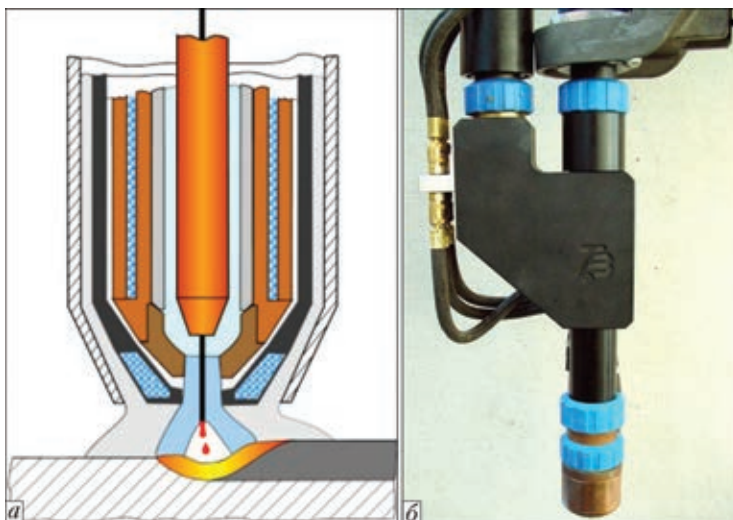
Схема процесса гибридной плазменно-дуговой сварки плавящимся электродом с кольцевым пустотелым анодом и аксиальной подачей электродной проволоки (а) и сварочная головка PLM 500 фирмы «ТБИ» для гибридной плазменно-дуговой сварки плавящимся электродом (б)
